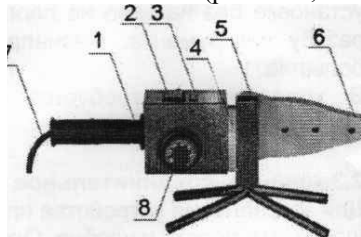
Електрозварювальний апарат для поліфузного зварювання Ритм ППТ-2000:
